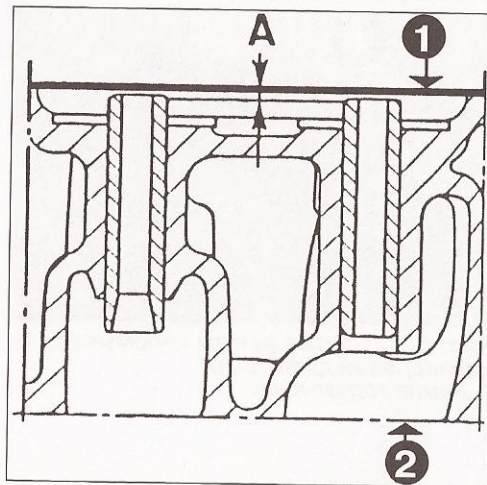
Частичный разрез головки блока цилиндров, показывающий расположение направляющих втулок клапанов.
